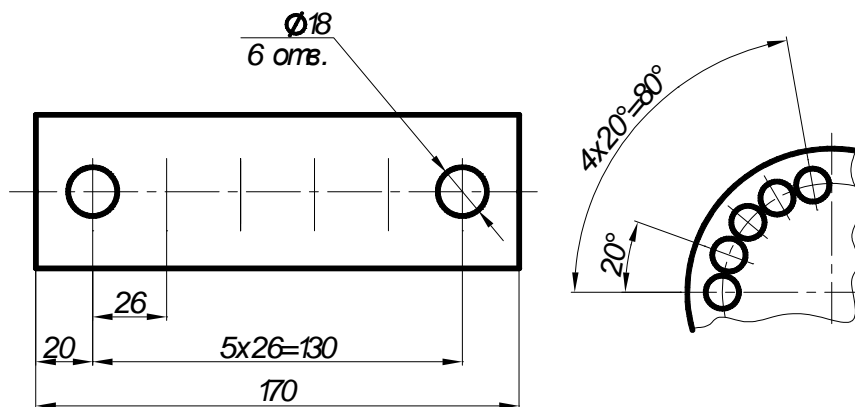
Нанесение размеров равномерно расположенных элементов
